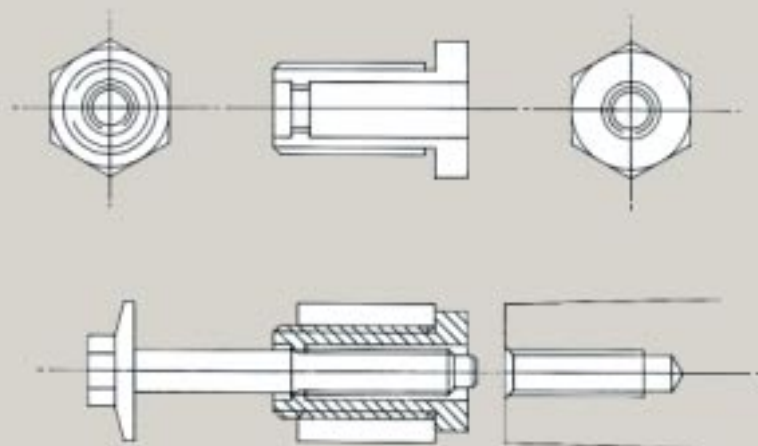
Oben: Toleranzausgleichsbuchse mit Innen- und Außengewinde. Unten: Im Auslieferungszustand ist die Schraube bis zum Ende des Schraubengewindes in die Buchse eingeschraubt
